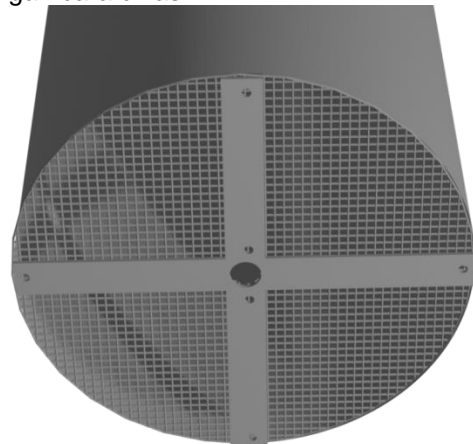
Sambungan Besi Plat dan Besi Plat Lubang
